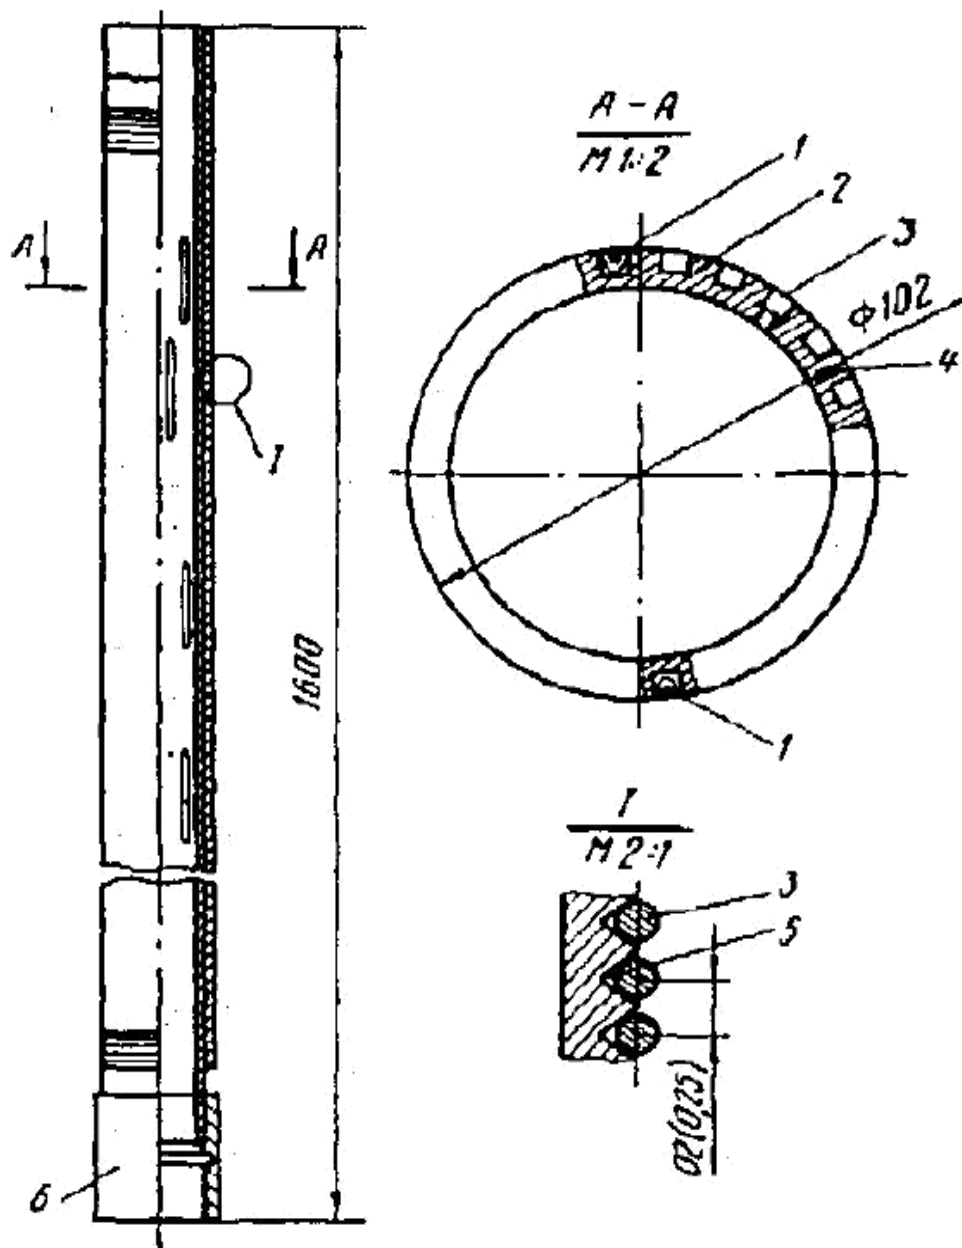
Секция фильтра проволочного однослойного: 1 – два продольных шва замка, выполненных пайкой; 2 – стингеры; 3 – проволочная набивка; 4 – трубчатый перфорированный силовой корпус; 5 – резьбовые канавки для укладки с гарантированным зазором проволочной набивки; б – соединительная муфта
